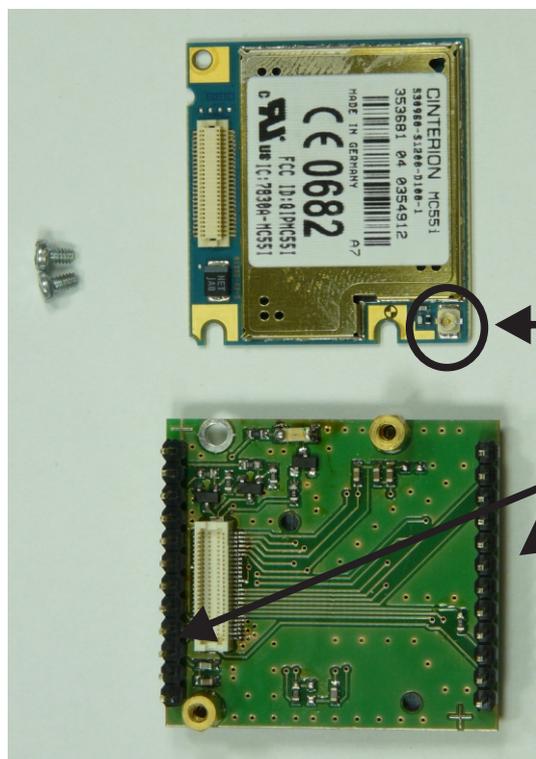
PCB – matična ploča sa SMT i Trough hole komponentama spremna za montažu.
